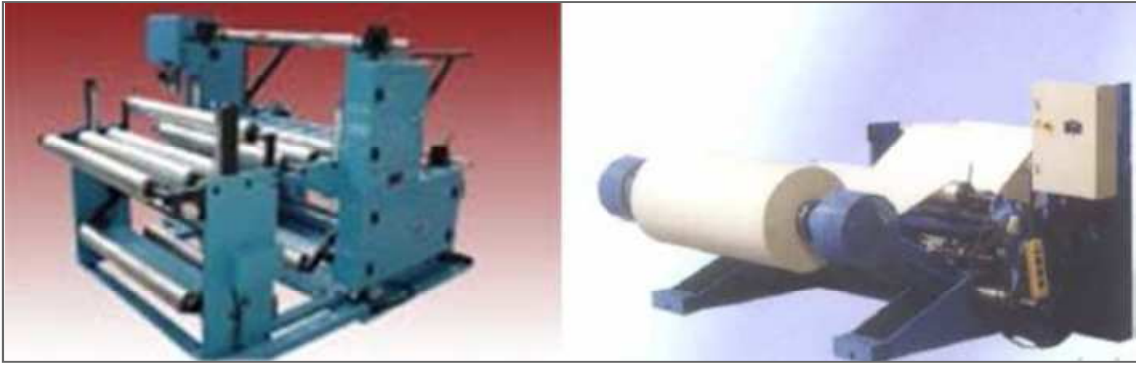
Esquema de una máquina rebobinadora horizontal central
